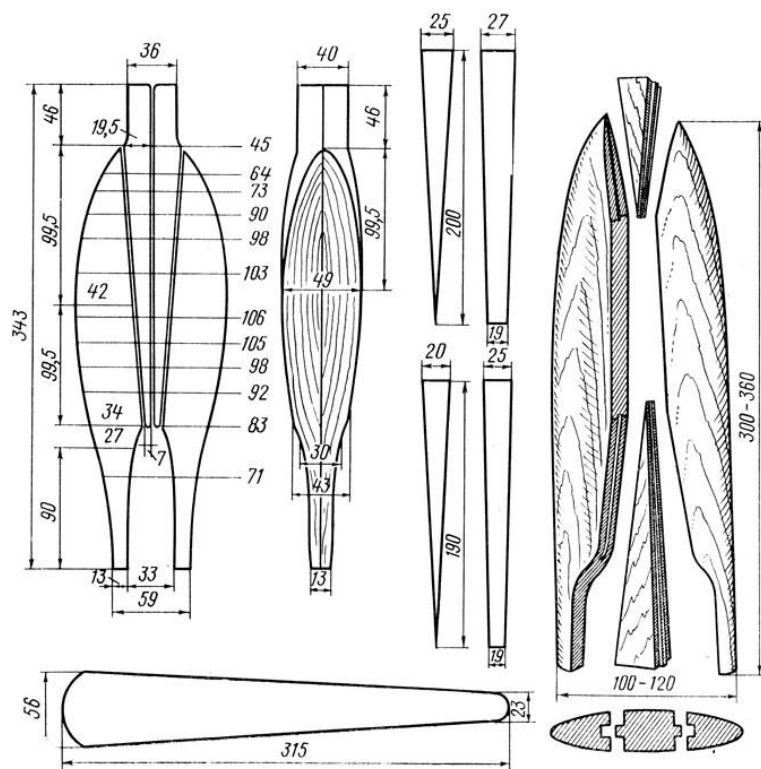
Правилка для шкурок соболя конструкции А.А. Елкова
